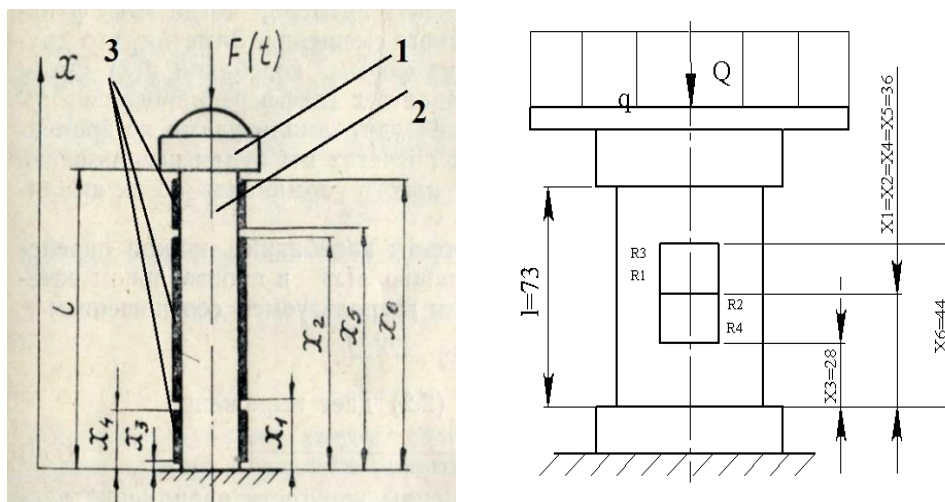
Розрахункова та конструктивна схеми ваговимірювального датчика
